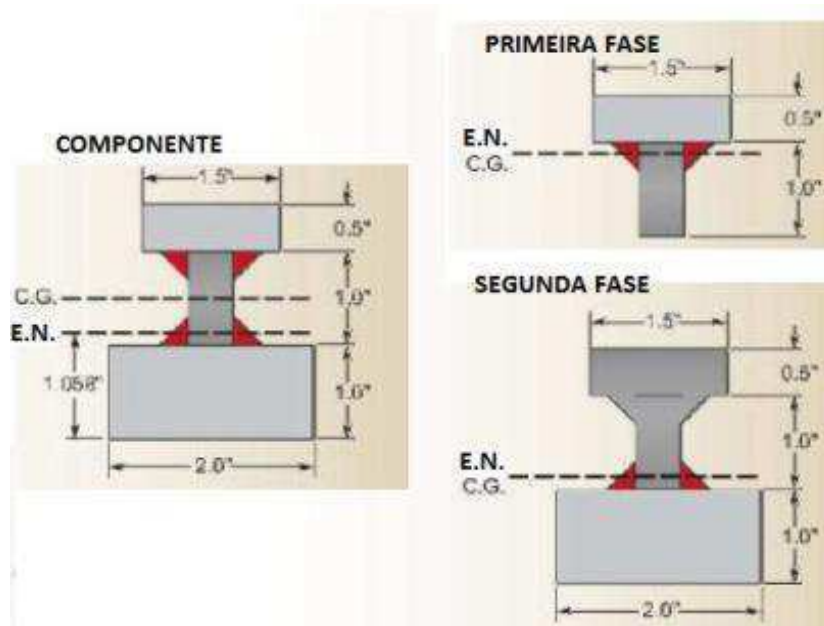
Soldagem de um componente não simétrico (Adaptado BLODGETT,2014).
